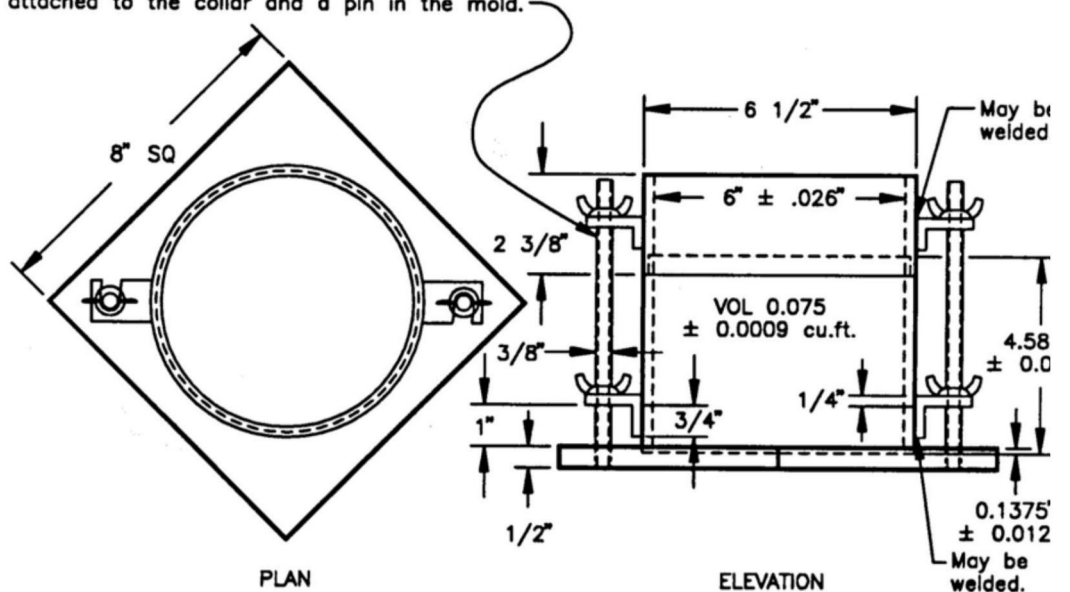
Figura F: Dimensiones del molde cilíndrico de 8 pulgadas. Fuente: ASTM D698
